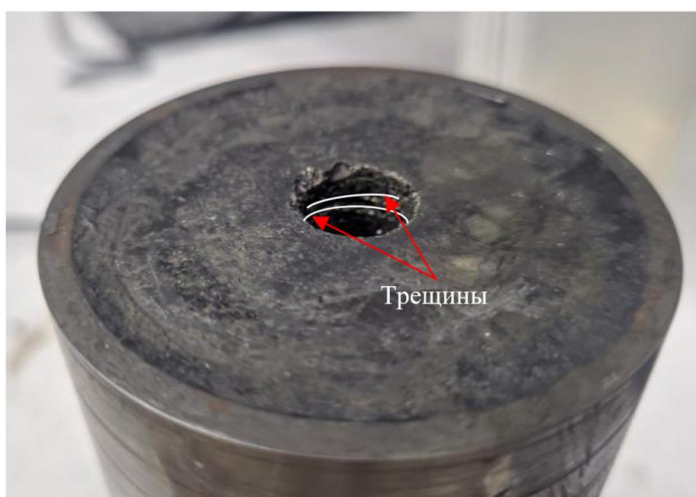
Трещины в образце, образовавшиеся в результате запрессовки
